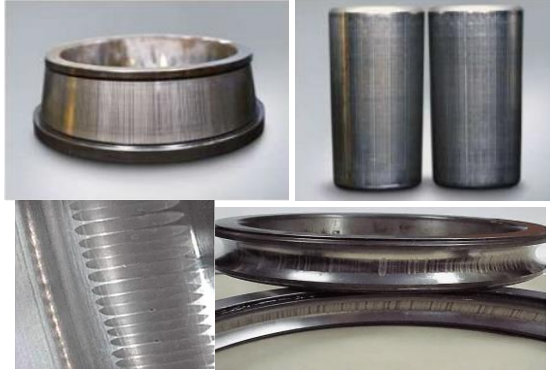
Повреждения подшипников, вызванные подшипниковыми токами.
